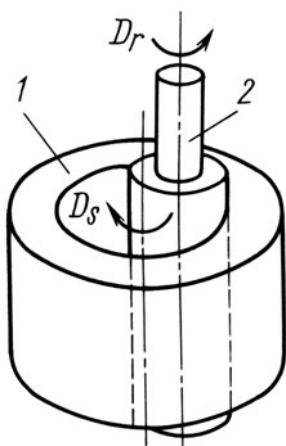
Схема планетарной обработки внутренней цилиндрической поверхности:
